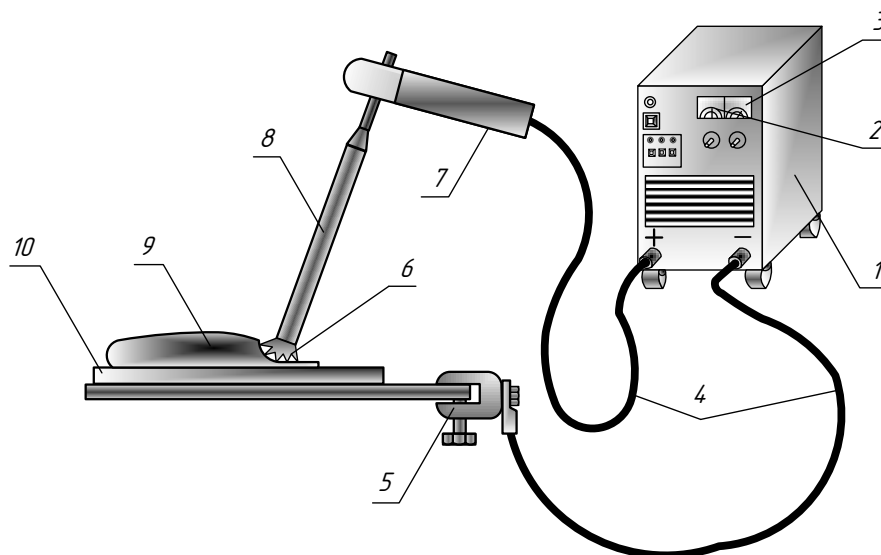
Схема ручной электродуговой сварки и наплавки:
